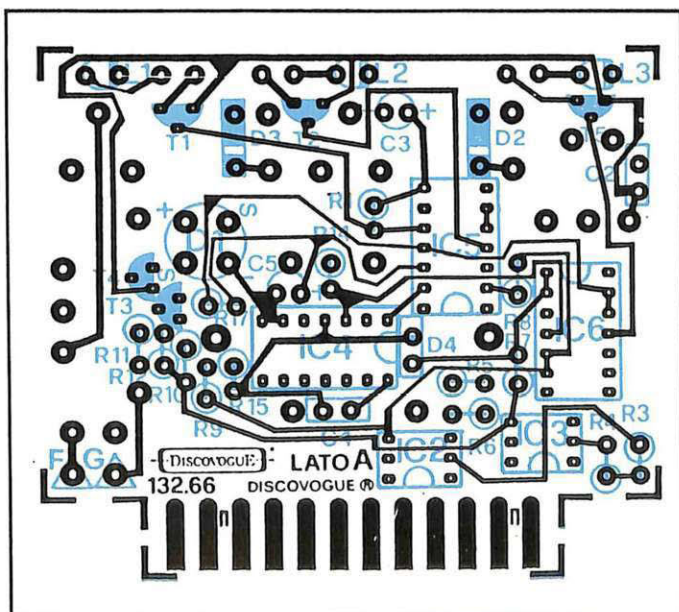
Pista conduttrice del lato A del circuito stampato principale con componenti montati.
